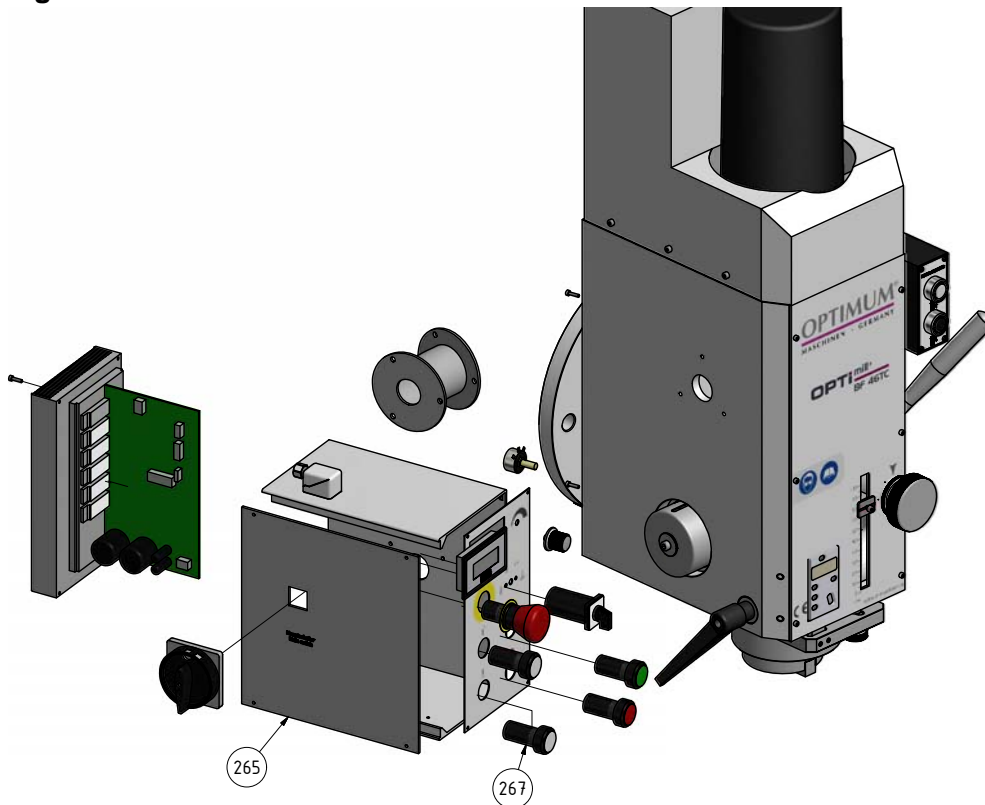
Fräskopf - Milling head BF46 TC Vario
